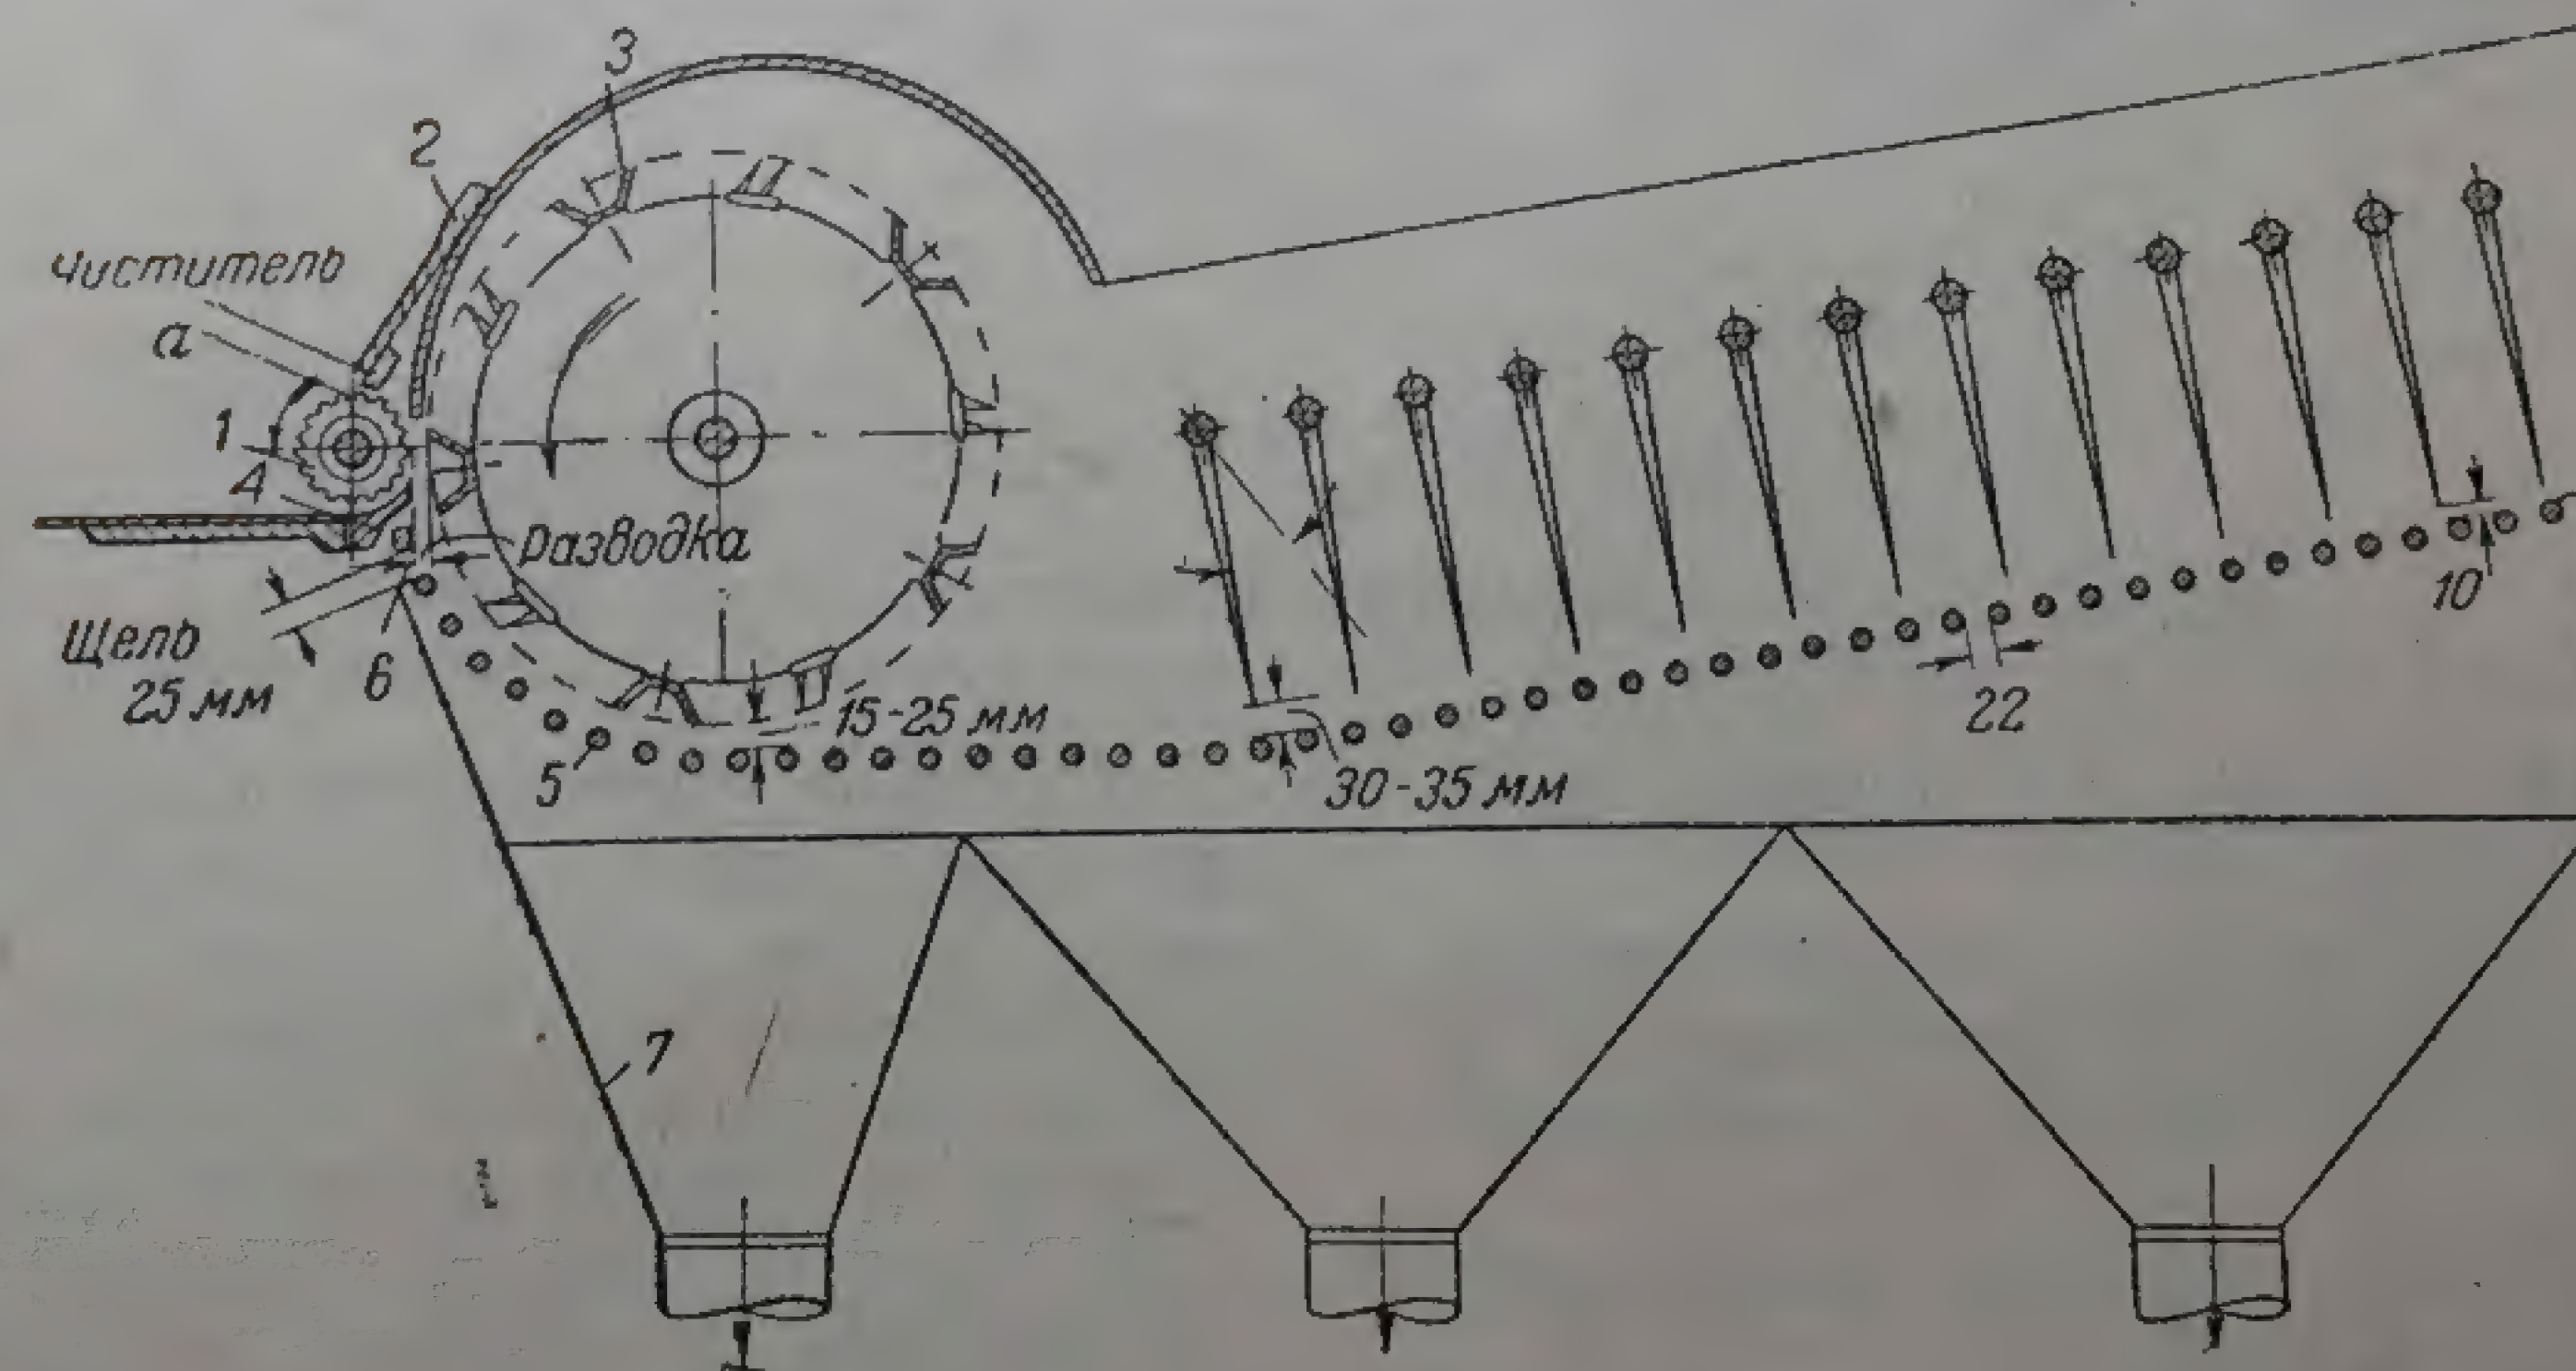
Паклеочиститель КП-1. Схематический разрез:
